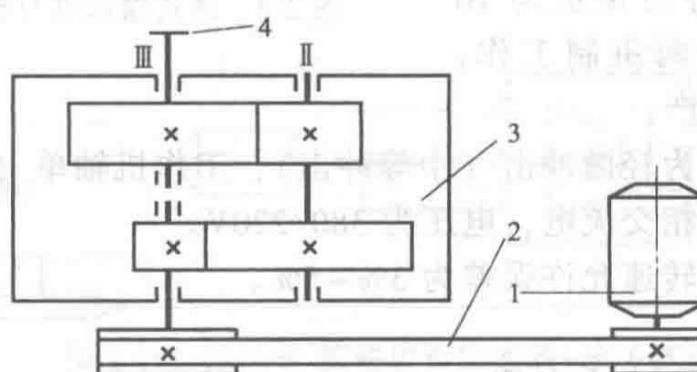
带传动+二级同轴式圆柱齿轮减速器
